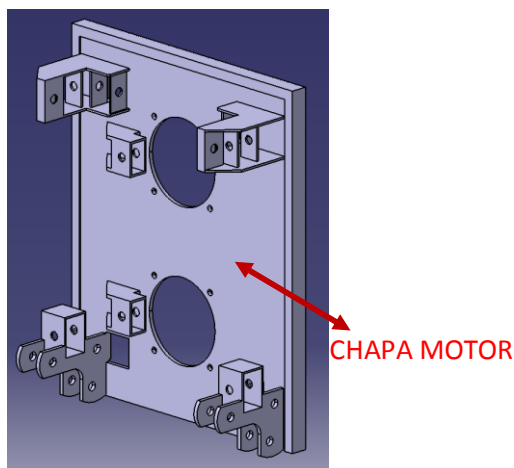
Conjunto soldado del grupo motor. Vista frontal 3D
